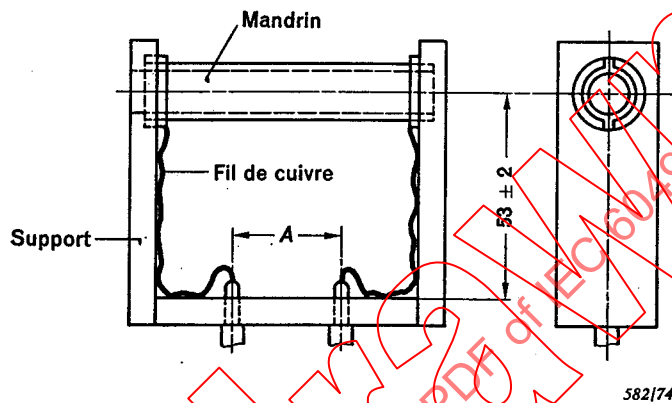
Exemple de support du mandrin (dimensions en mm).
